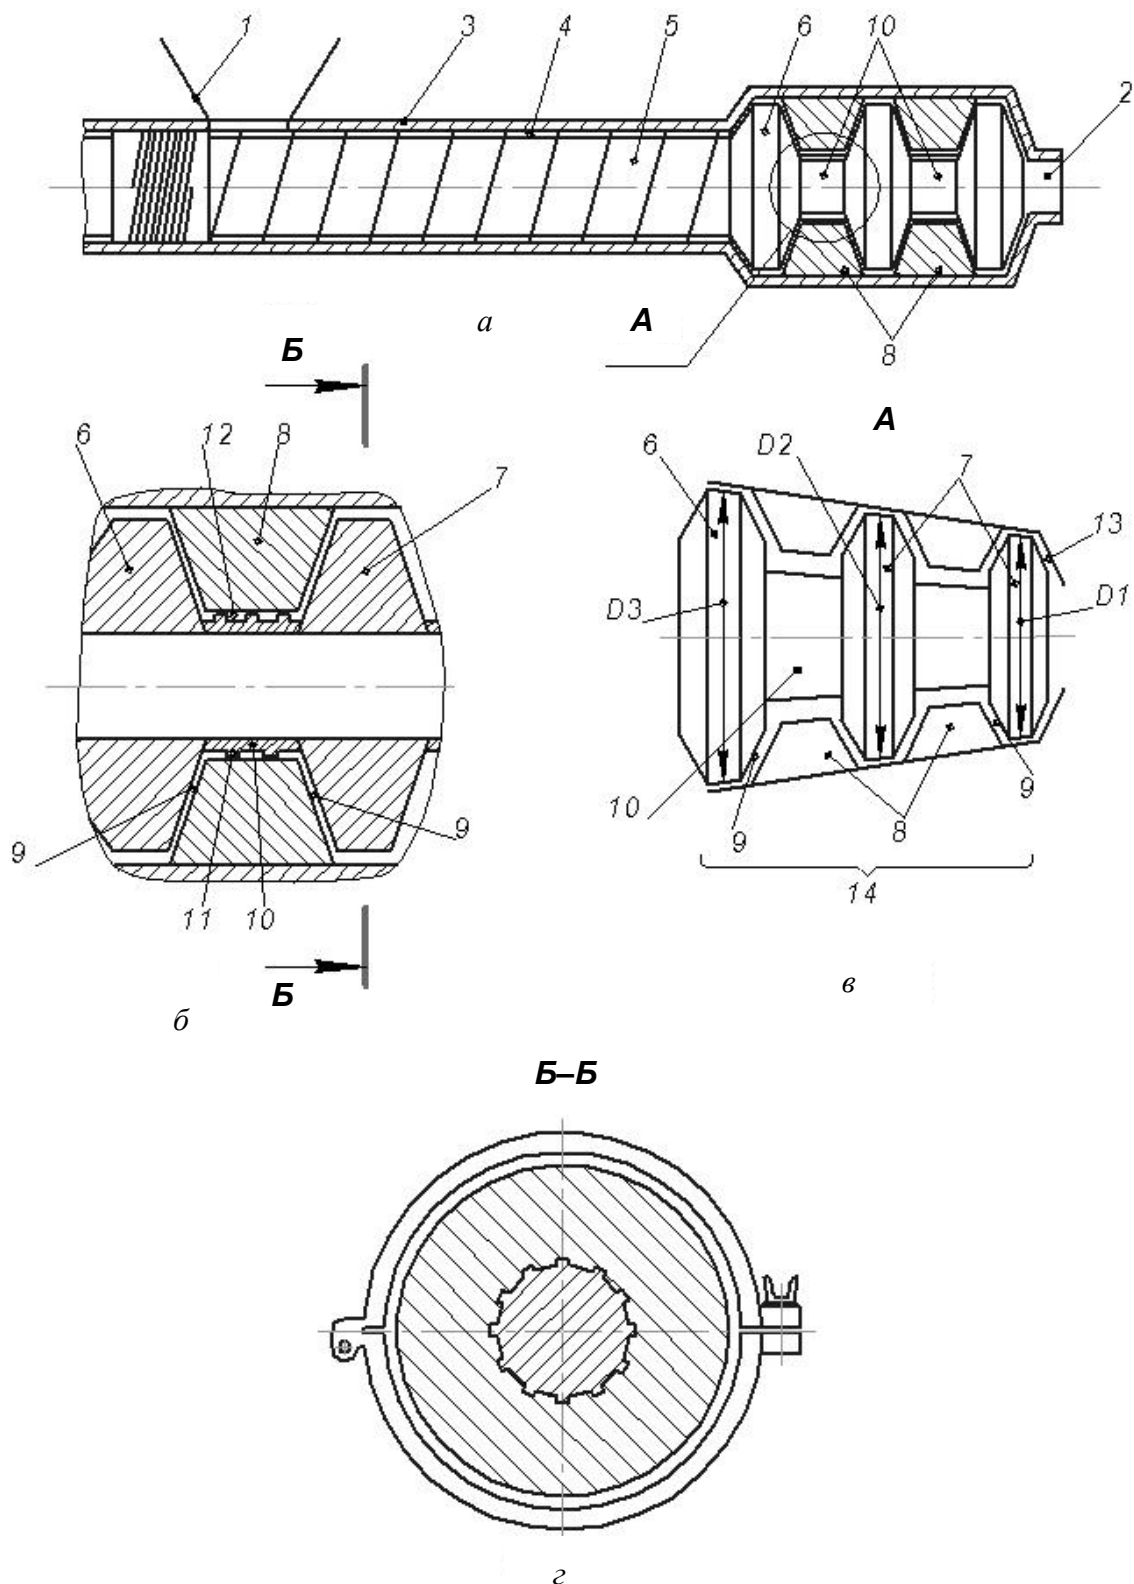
Конструкції дискового екструдера зі складеним обертовим диском (пат. України № 27461 U [42]): 1, 2 – завантажувальний і розвантажувальний отвори, відповідно; 3 – корпус; 4 – порожнина корпусу; 5 – черв’як; 6 – основний диск; 7 – додатковий диск; 8 – нерухомий диск; 9 – канал; 10 – дистанційна втулка; 11 – зовнішня гвинтова нарізка; 12 – канал; 13 – конічна твірна; 14 – ділянка розташування нерухомих дисків
